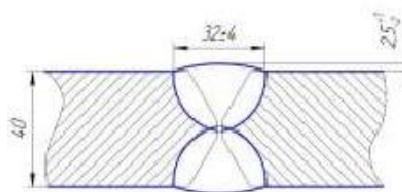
Конструктивные размеры сварного шва
